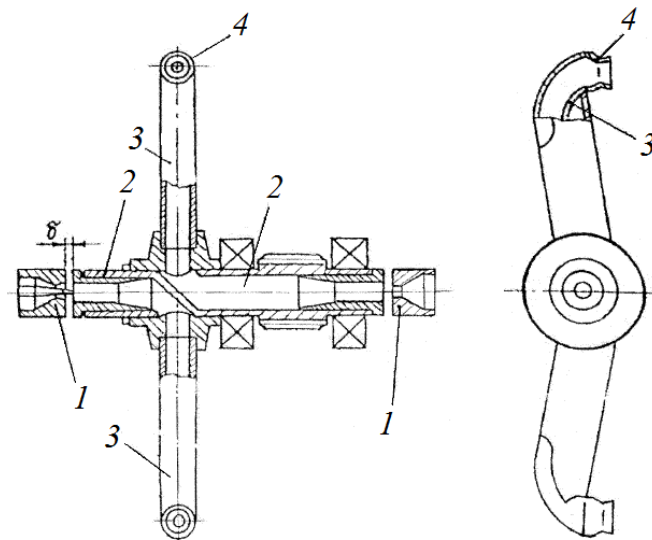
Конструктивна схема реверсивної струменевої реактивної турбіни [26]:
